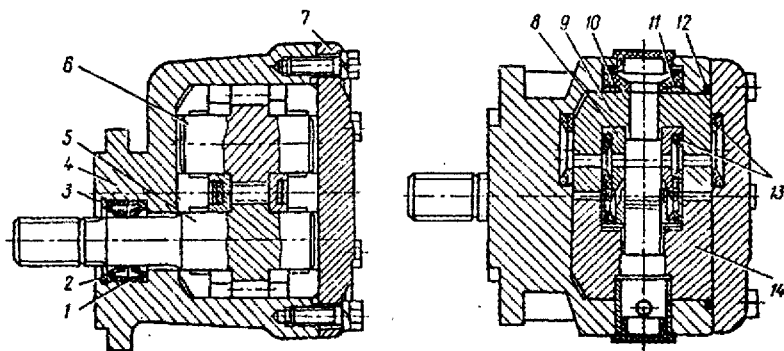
Насос НШ-32-3: 1 и 10 – манжеты; 2 – опорное кольцо; 3 – стопорное кольцо; 4 – корпус насоса; 5 и 6 – ведущая и ведомая шестерни; 7 – крышка; 8 – пластик; 9 – поджимная обойма; 11 – опорная пластина; 12 – уплотнительное кольцо; 13 – торцевые манжеты; 14 – подшипниковая обойма
